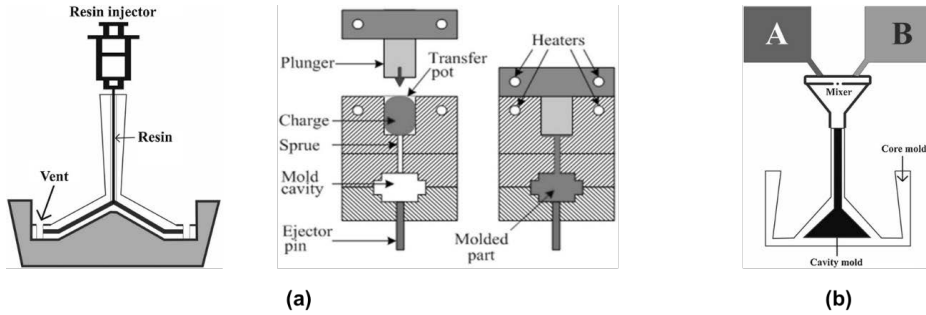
Esquema del método de moldeado por infusión de resina para la obtención de PMC. Fuente: [21].
